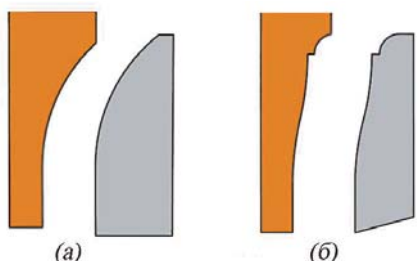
Филинчатые фрезы с вертикальным расположением ножей: а — 012.08.00.00.000; б — 012.09.00.00.000
